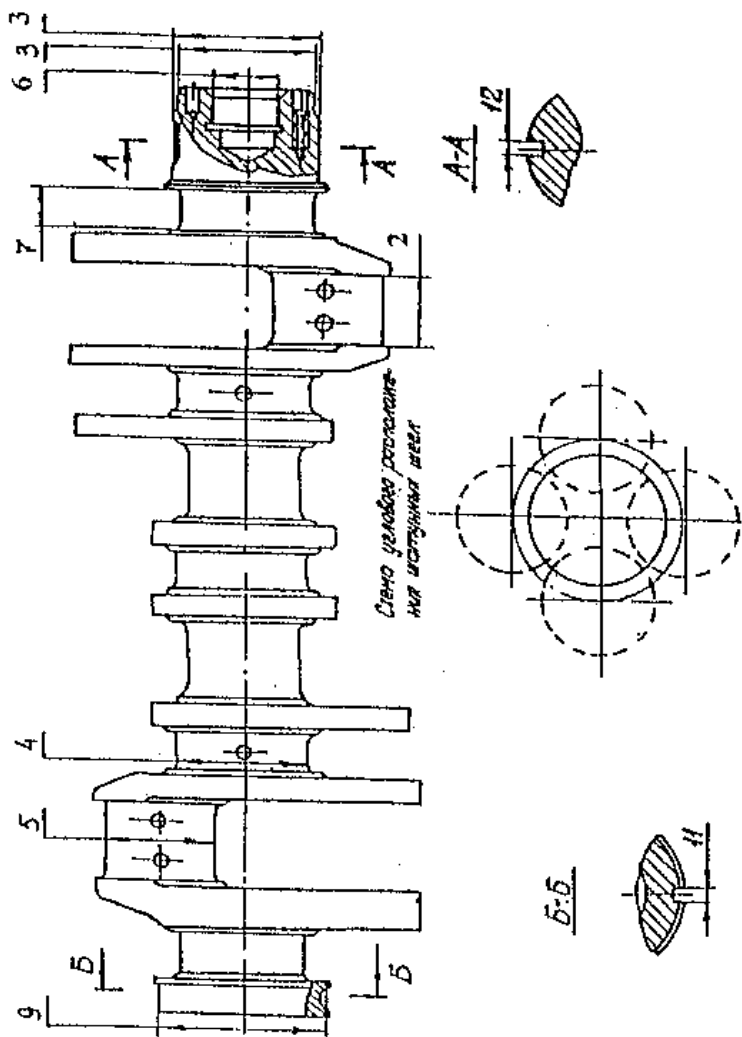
Коленчатый вал КамАЗ-740. Материал: Сталь 40ХНМ.
